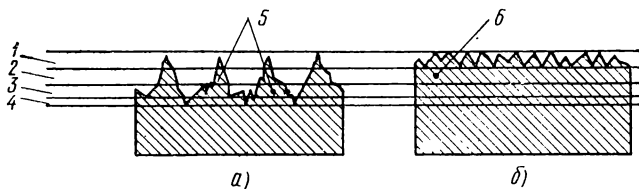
Следы резов после зубофрезерования с различными подачами:
